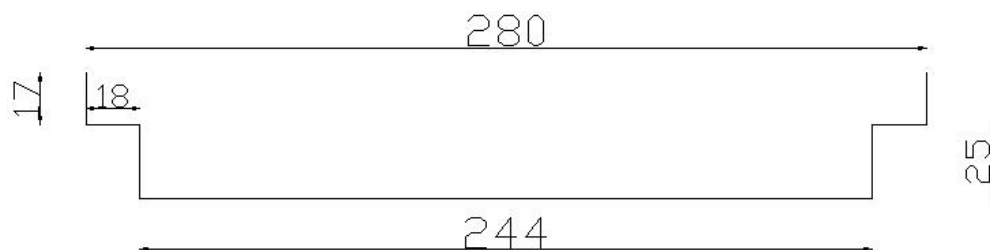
Dimensiones del recipiente para ensayos (en milímetros).
